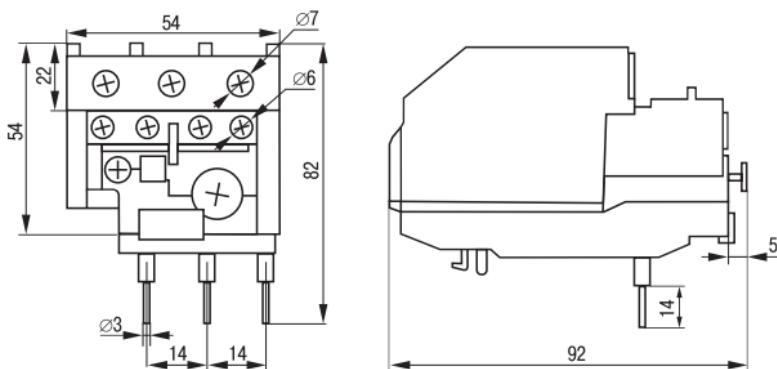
Габаритные и установочные размеры реле РТИ-2355
